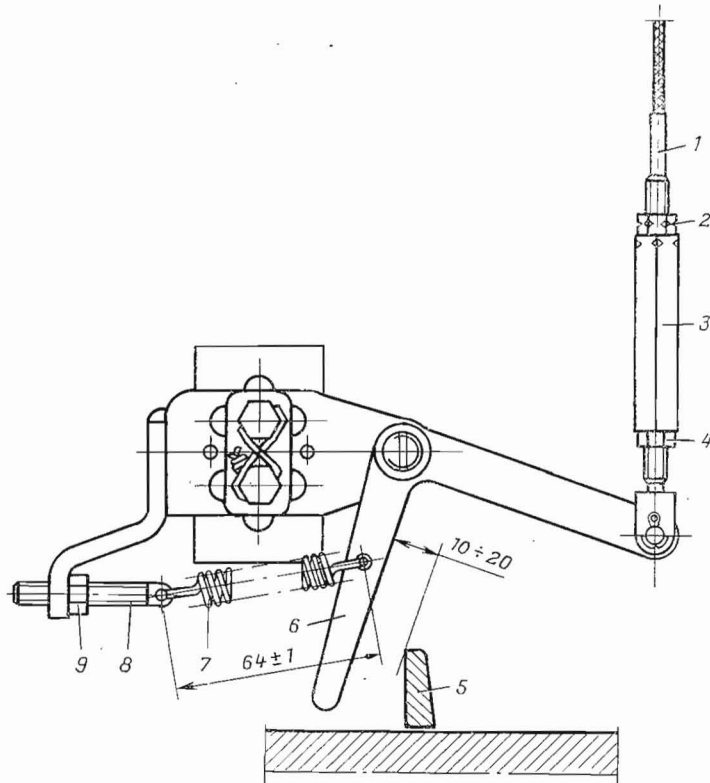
Регулировка тросового привода рычага сброса защелки улавливателя:
